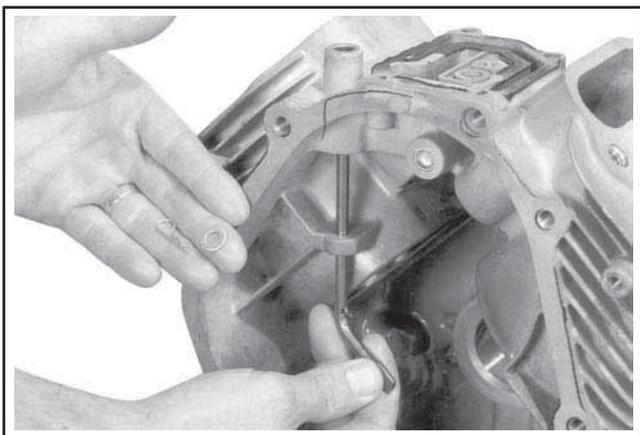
Installation du petit arbre transversal du régulateur de 6 mm.
